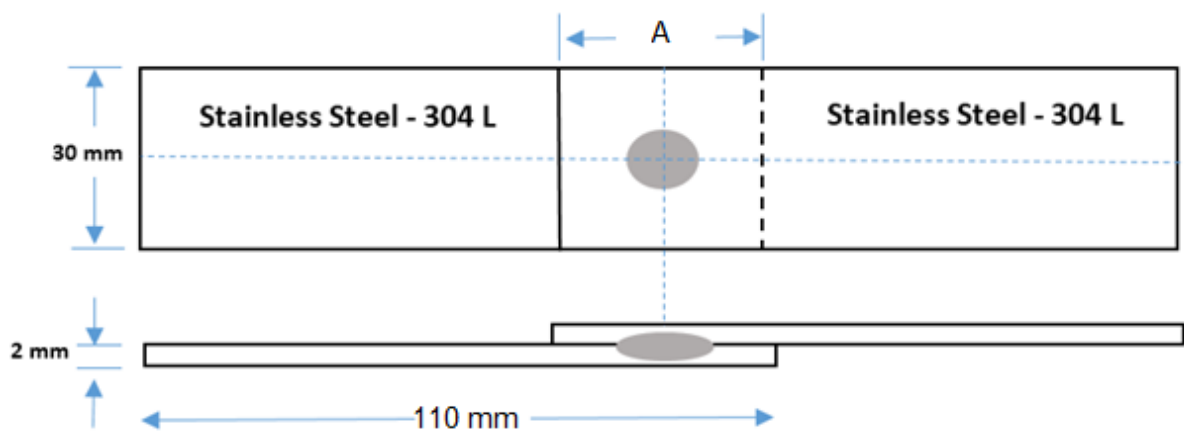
Dimension des assemblages réalisés par soudage par point
